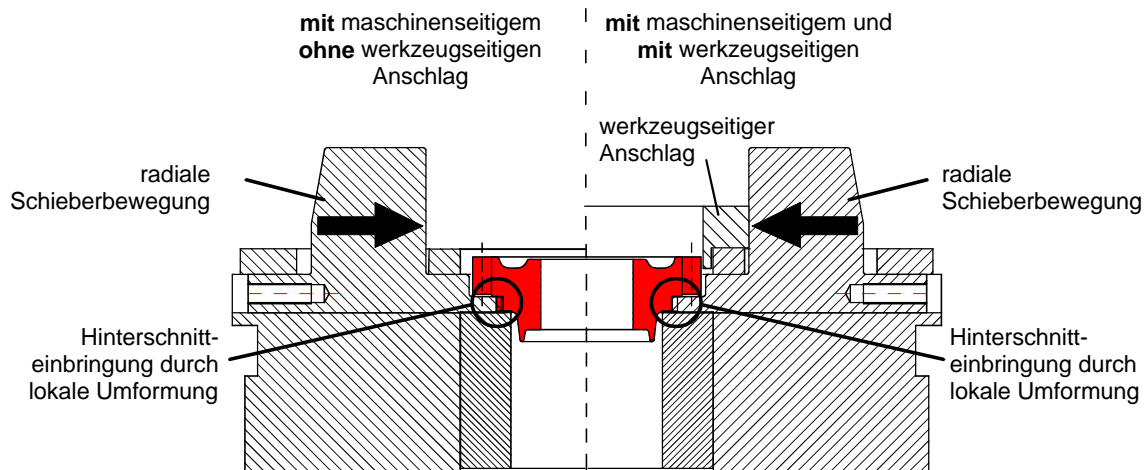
Werkzeugprinzip der zweiten Umformstufe mit und ohne werkzeugseitigem Anschlag
